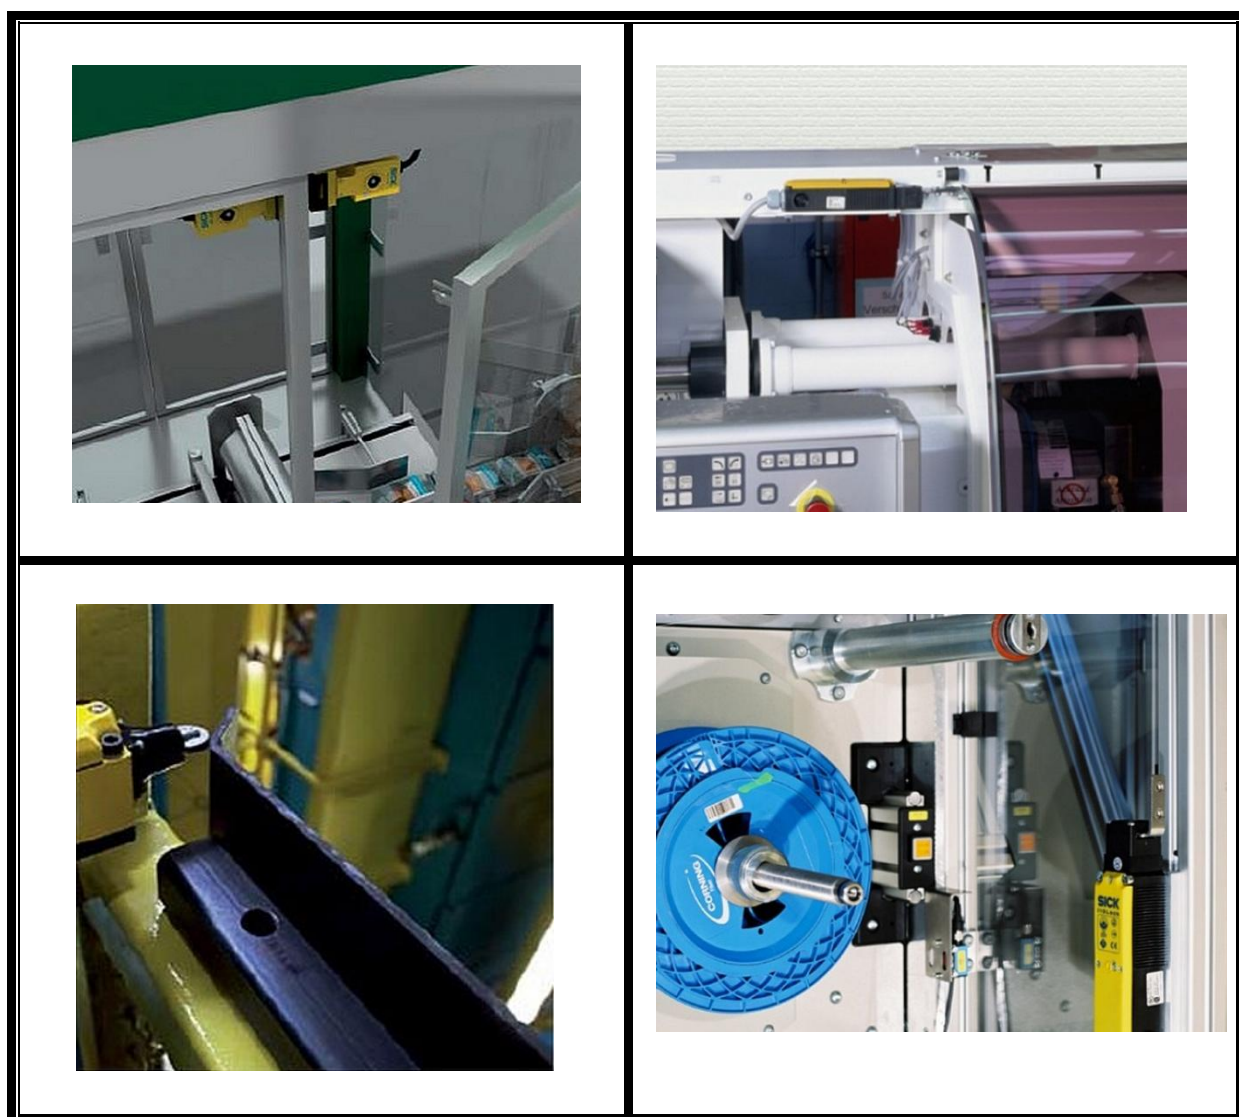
Instalace spínače s plunžrem a), s kladkou b) [3]
